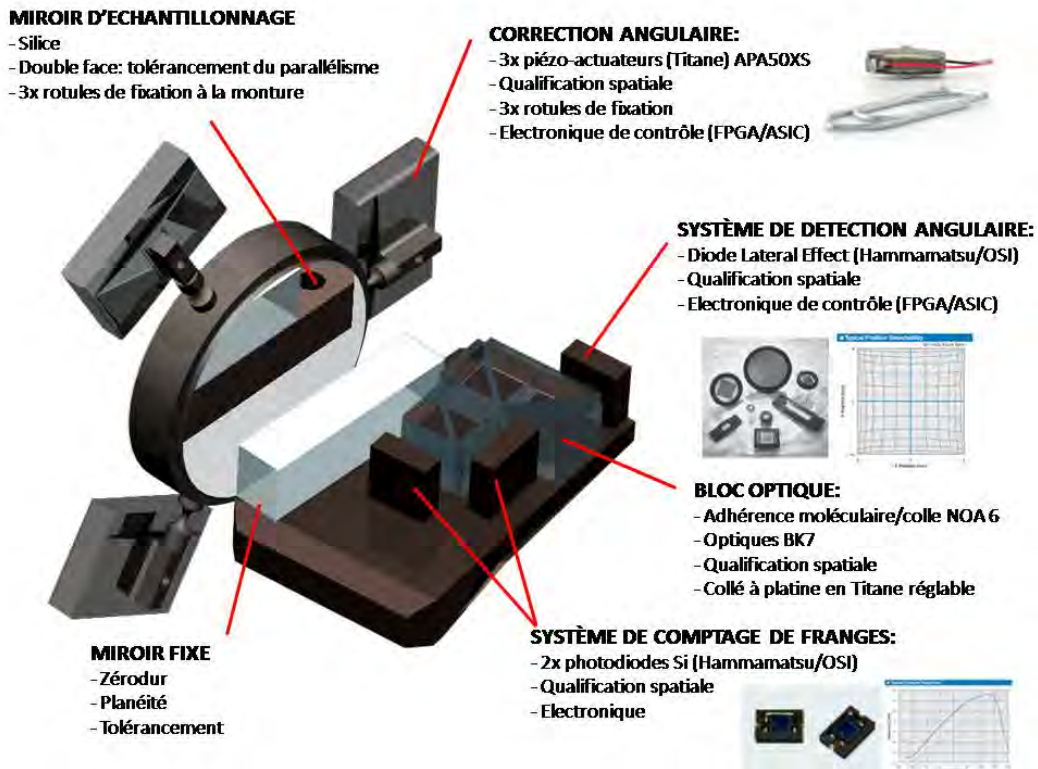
Vue d'ensemble des différents composants du mini-banc optique de métrologie *IFTSUV*.
